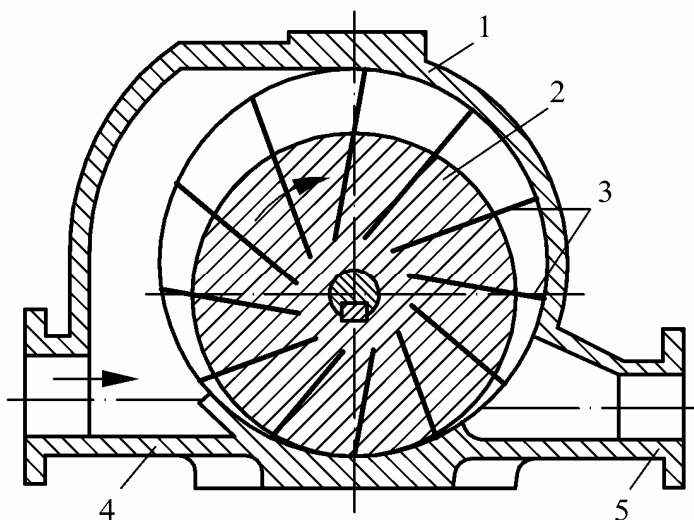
Конструктивная схема роторного компрессора: 1 – корпус; 2 – ротор; 3 – пластины; 4 – всасывающий патрубок; 5 – подающий патрубок
